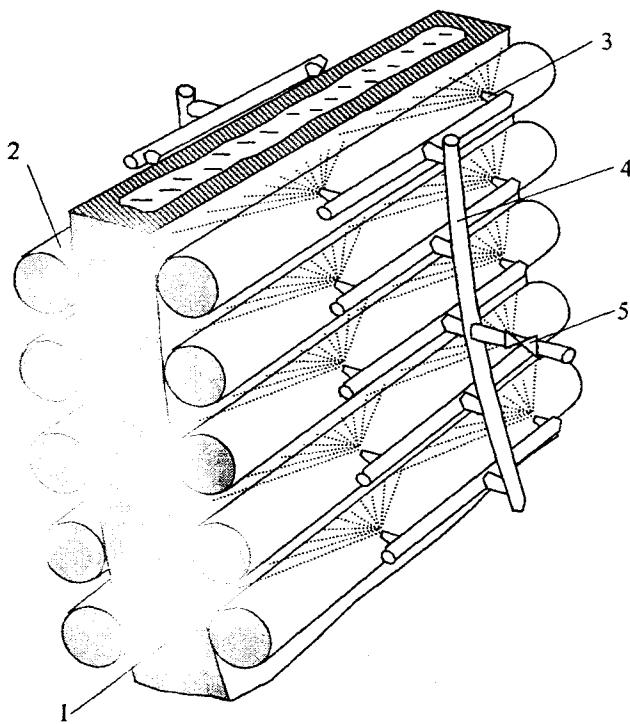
Схема вторичного охлаждения слябовой непрерывнолитой заготовки:
